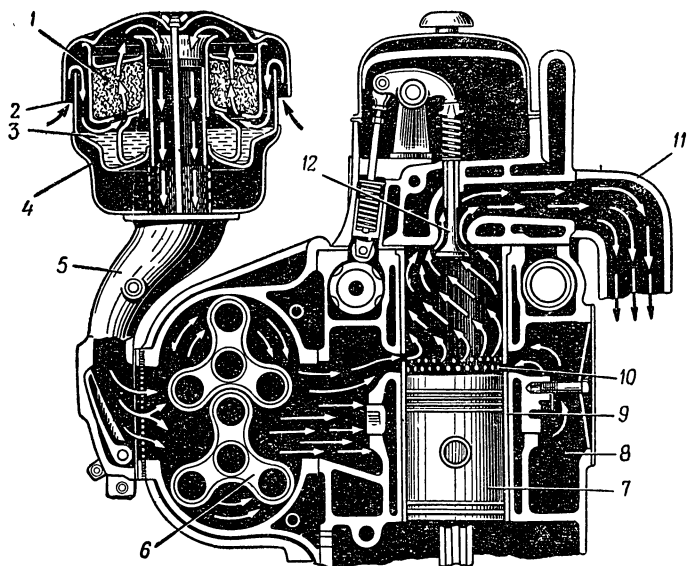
Воздухоочиститель и схема продувки дизеля ЯАЗ-204:
